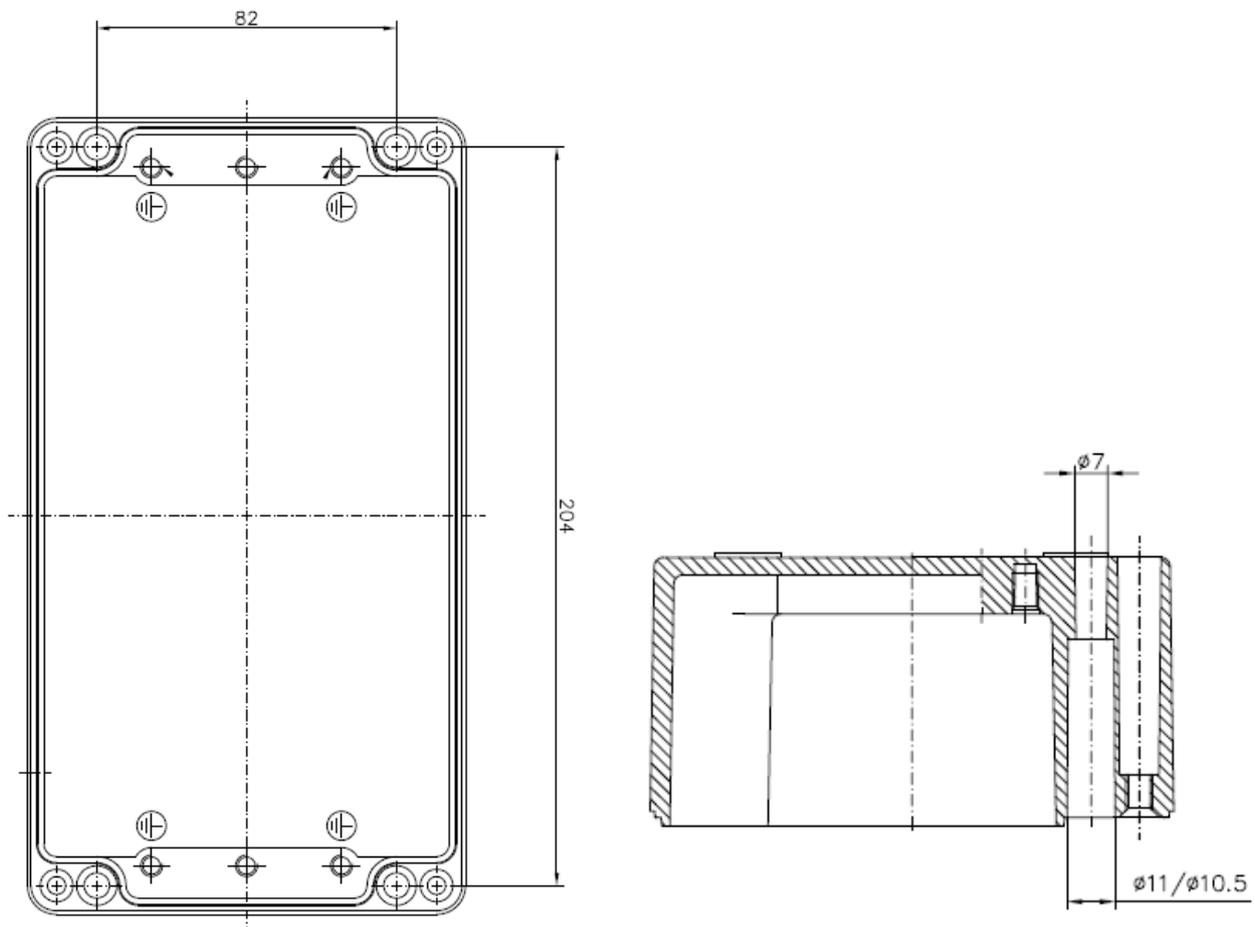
Bohrungen und Befestigungsschrauben für die Installation der Zentraleinheit
